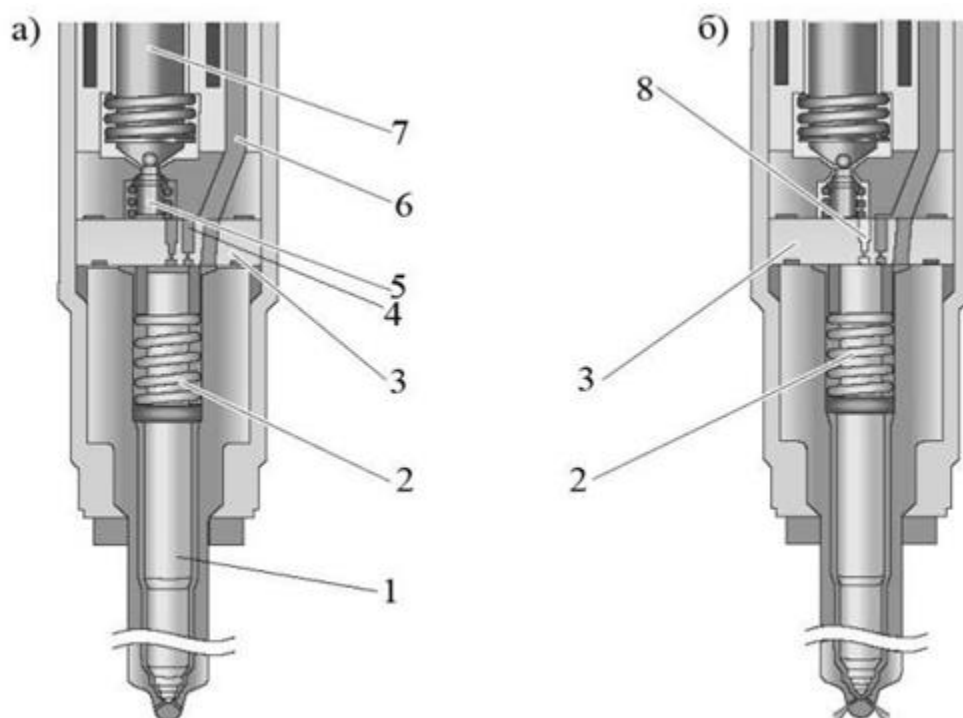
Принцип работы форсунки :1 – игла форсунки; 2 – пружина форсунки; 3 – пластина дросселя; 4 — впускной дроссель; 5 – плунжер клапана; 6 – линия высокого давления; 7 соединительный элемент; 8 – выпускной дроссель; а – форсунка закрыта; б — форсунка открыта
